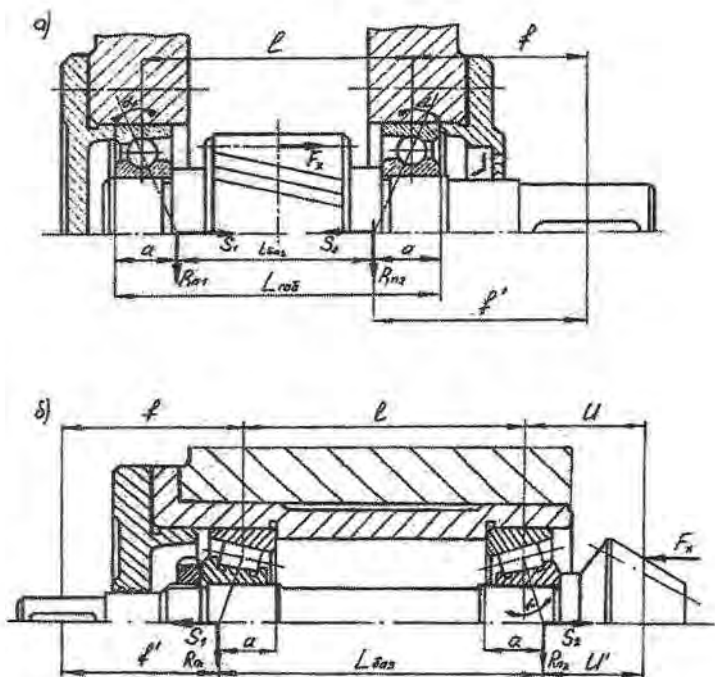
Схемы установки радиально-упорных подшипников в узлах:
